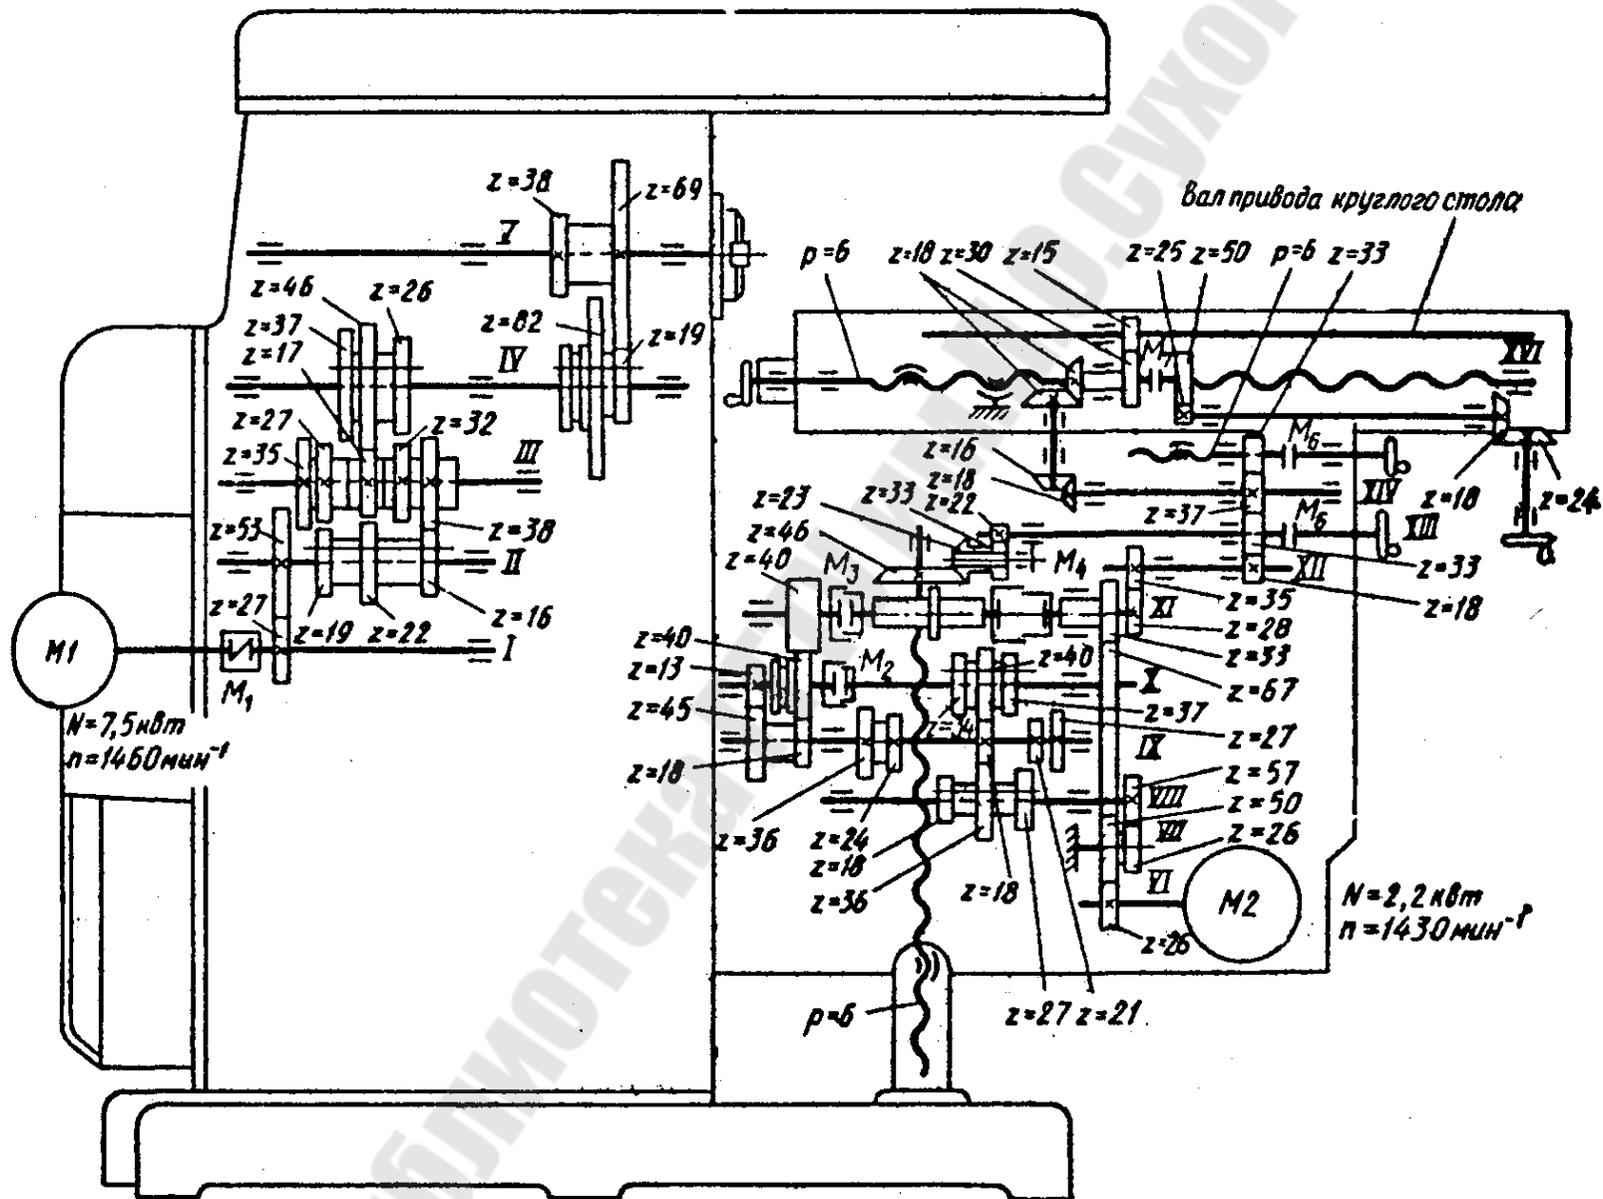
Кинематическая схема горизонтально-фрезерного станка
